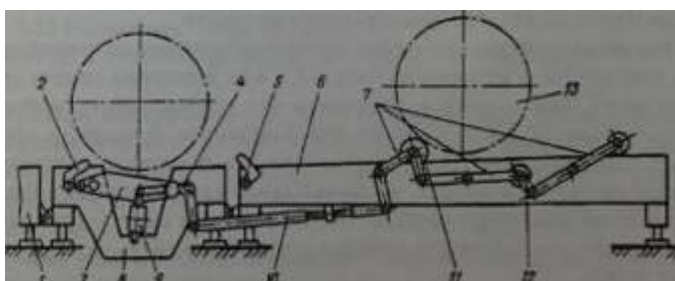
Схема отсекателя установки ПАУ-1001В: 1 - покатки скатывания; 2, 3, 4 - рычаги; 5 - мостик отсекателя; 6 - покатки накопителя; 7 - рычаги; 8 - корпус; 9 - домкрат; 10 - тяга; 11 - ограничитель; 12 - ролик; 13 – труба
